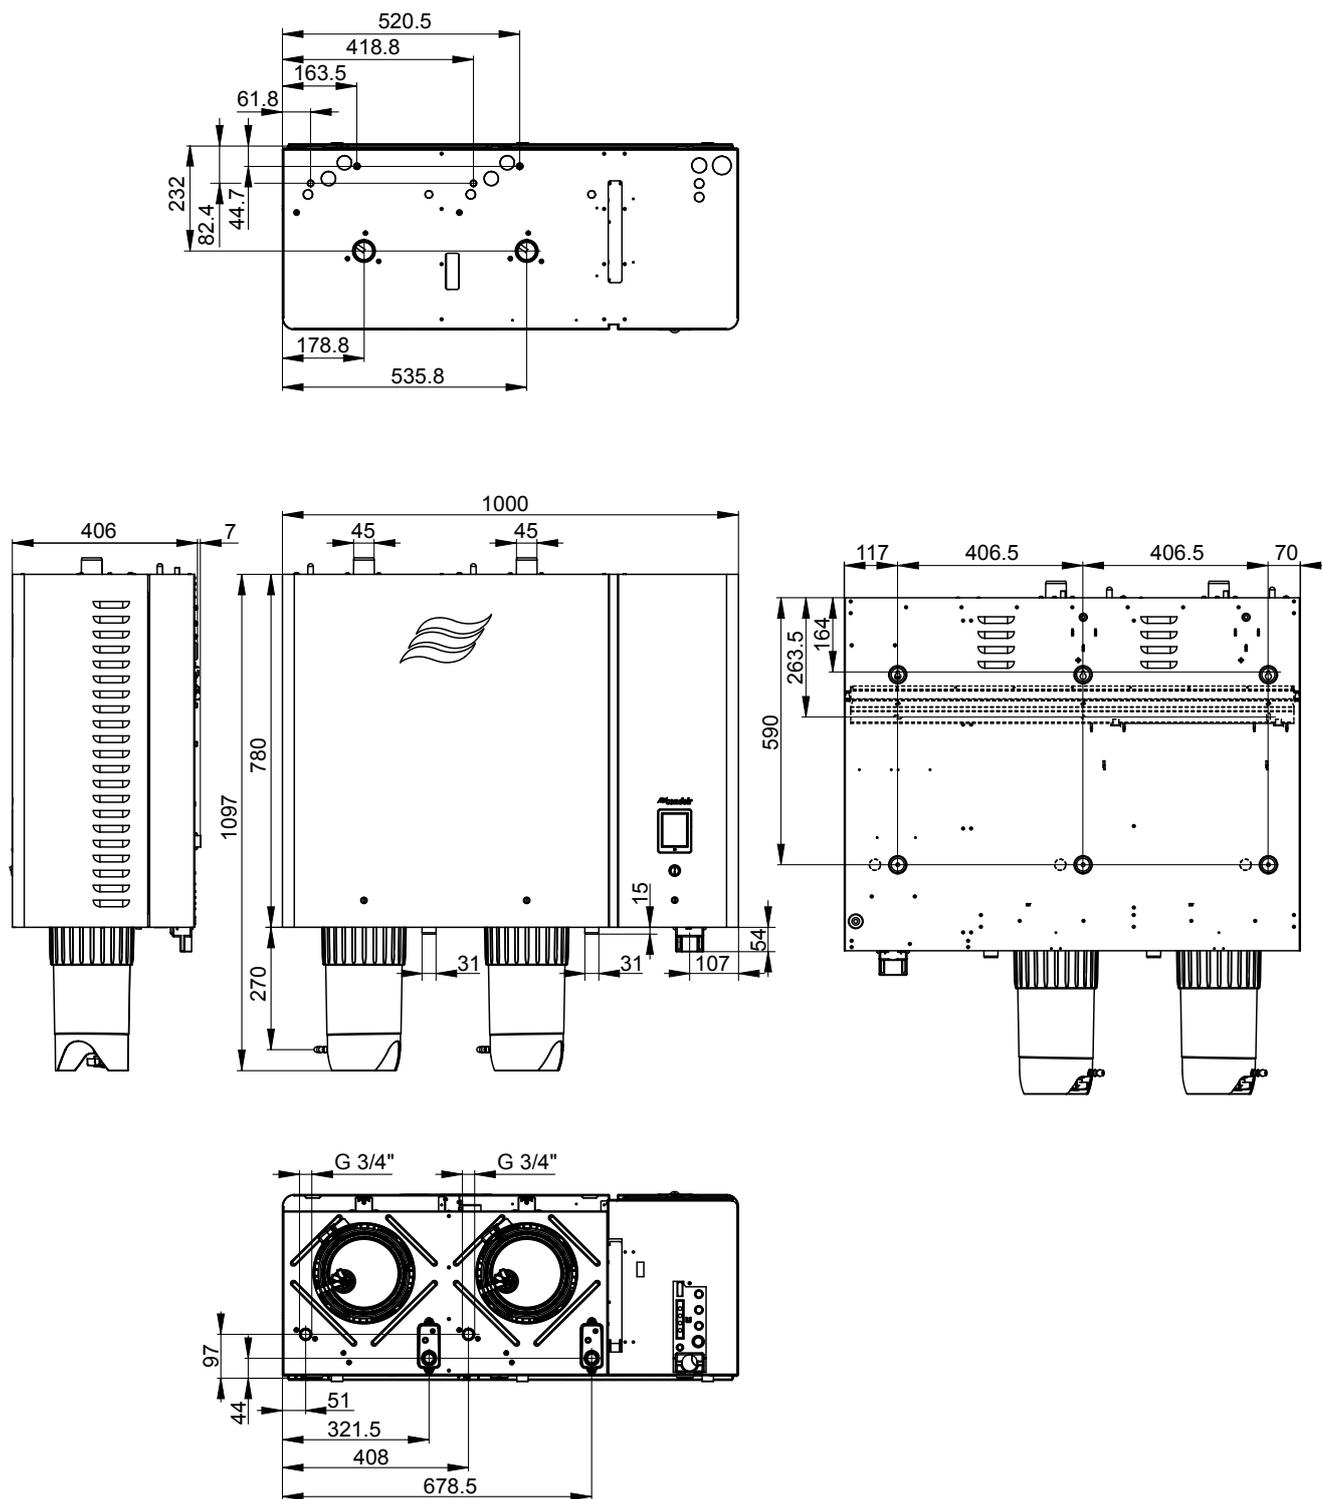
Dimensioni del modulo "L" (misure in mm)
